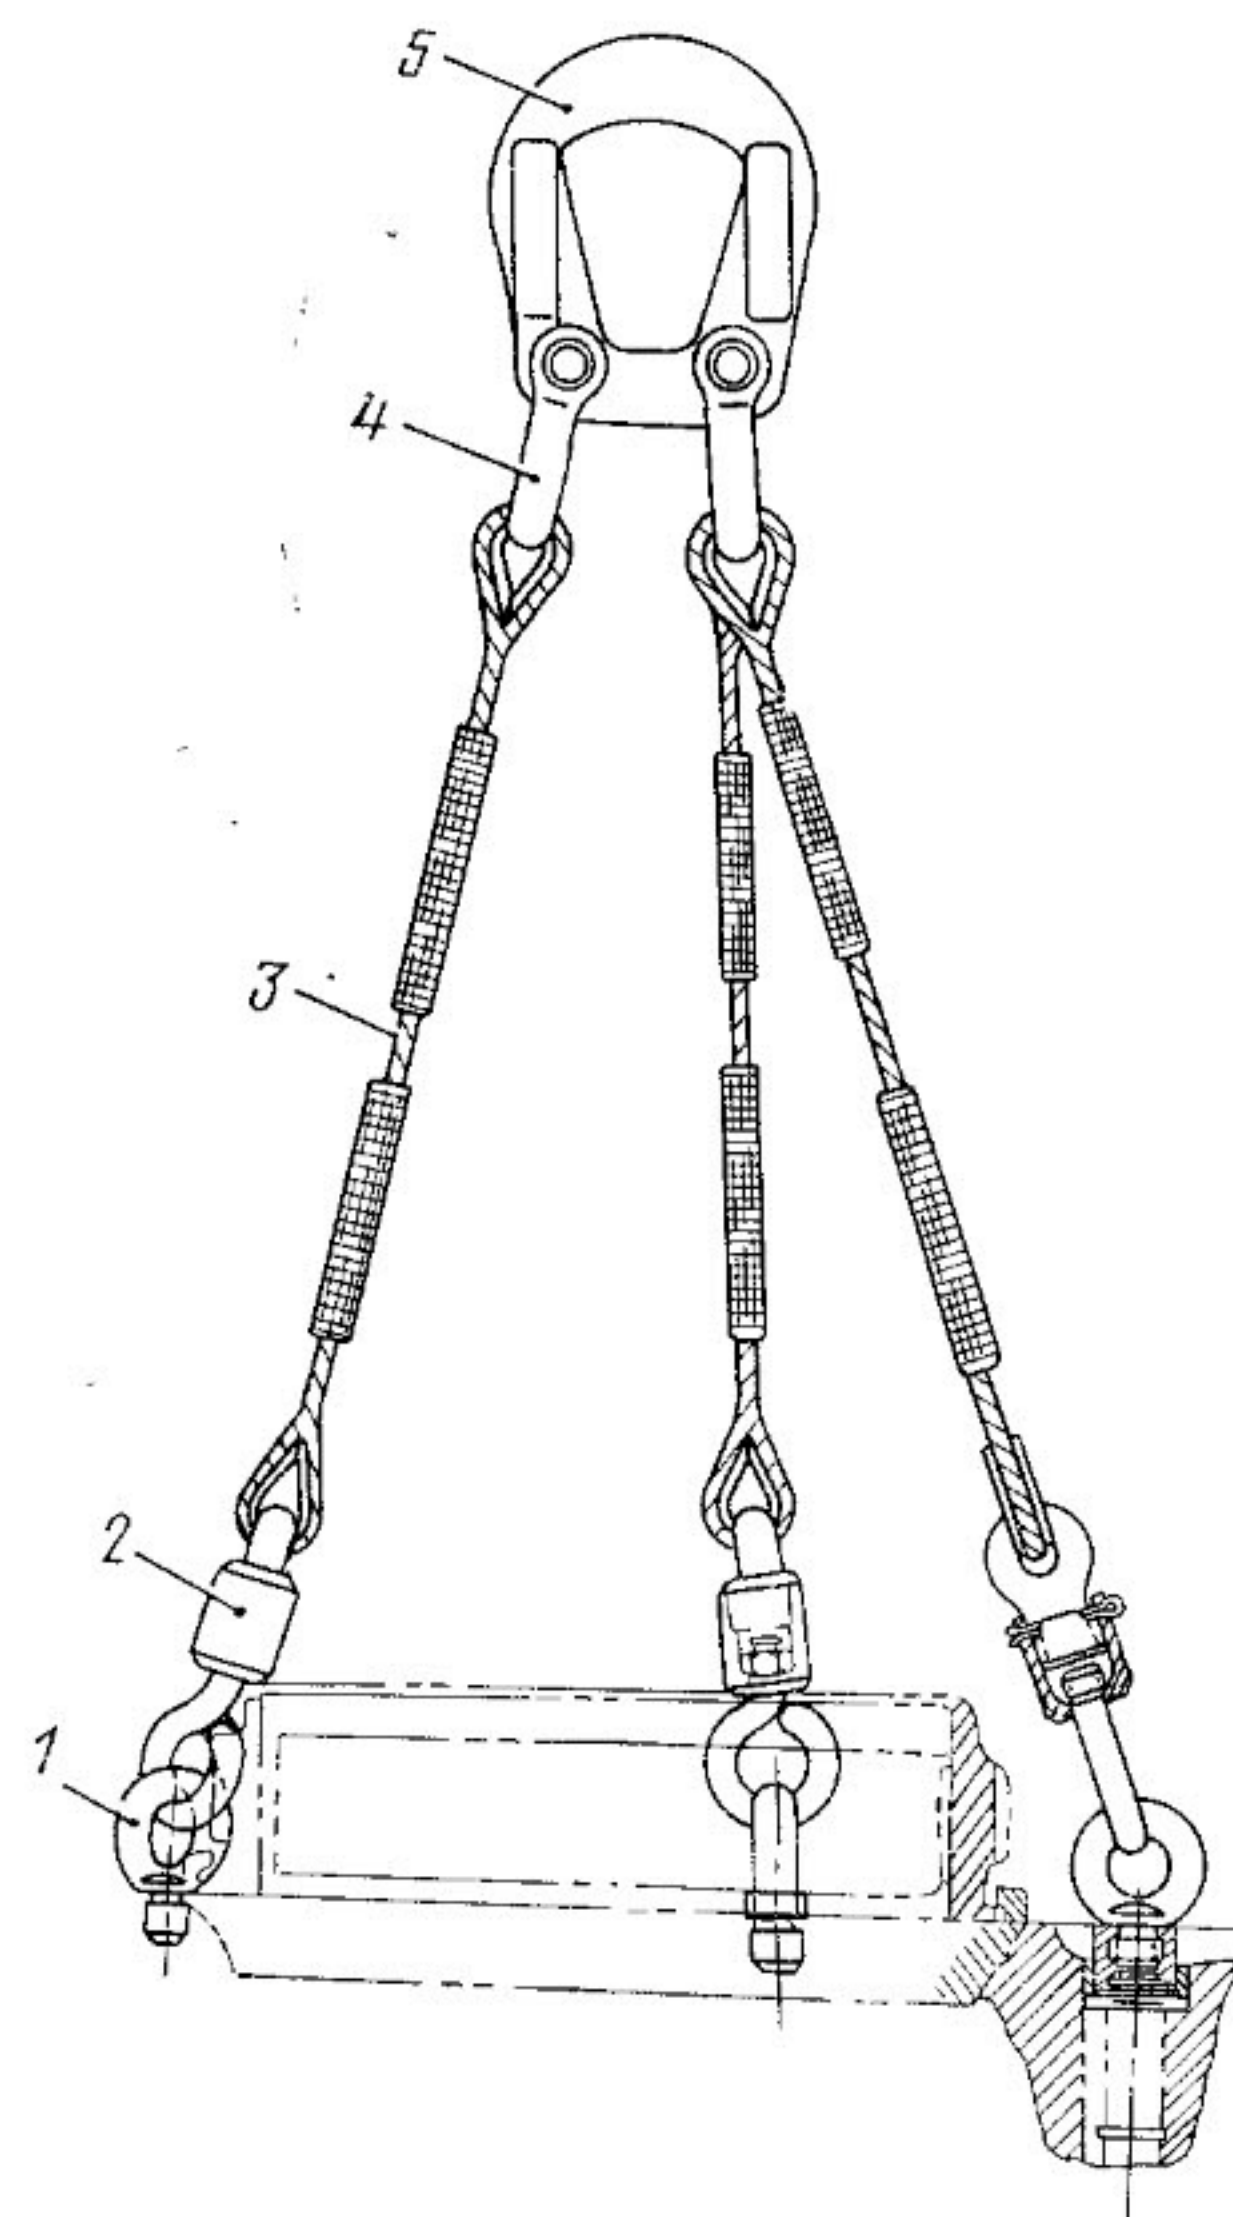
Стропы для подъема втулки несущего винта и гидроключа:
